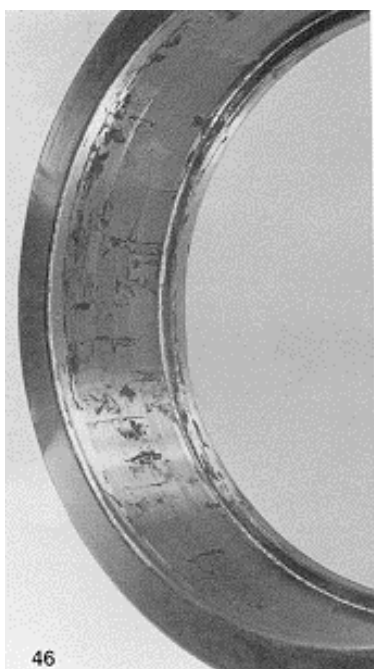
Следы коррозии на наружном кольце цилиндрического роликоподшипника
